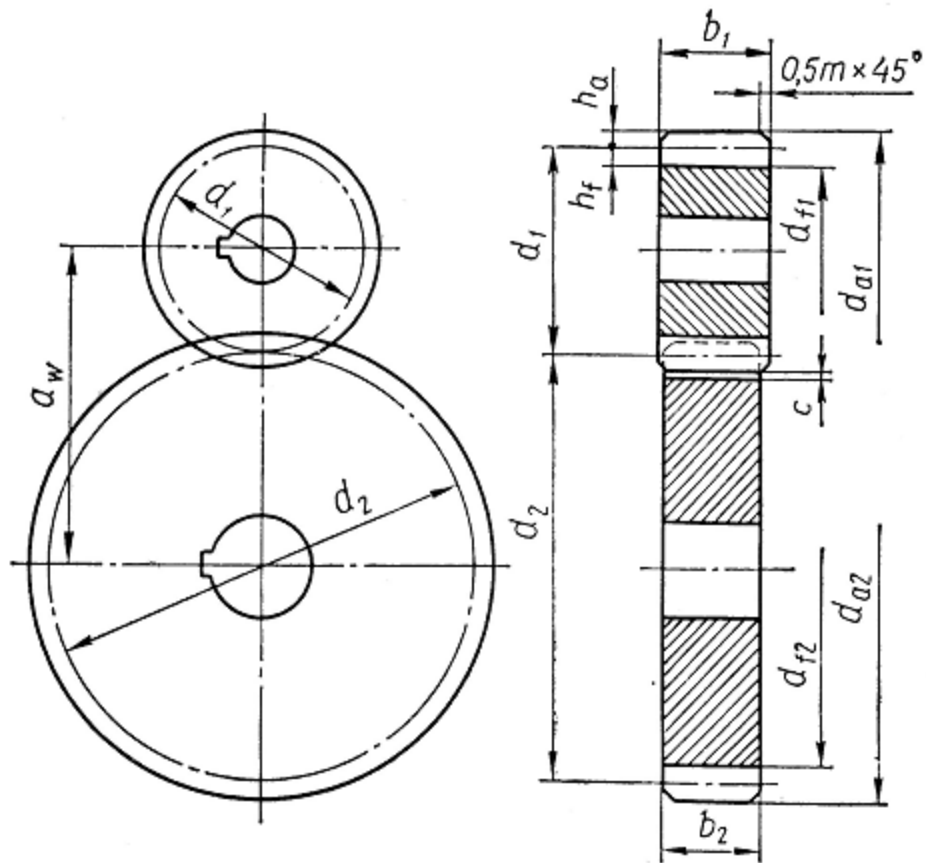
Розрахункова схема зубчастої передачі приводу каруселі фасування
